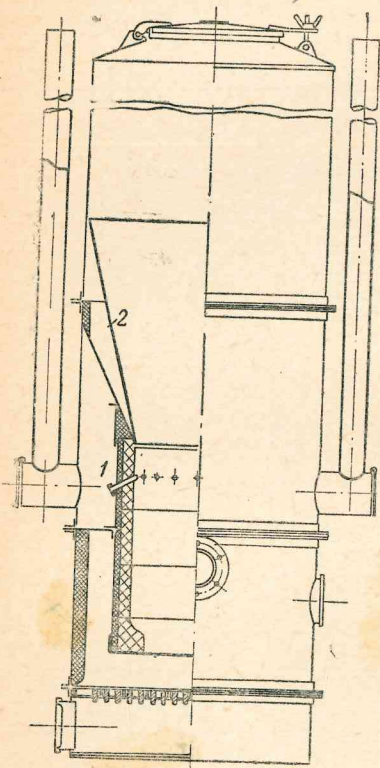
Приспособление газогенератора МСВ-84 для работы на швырке
